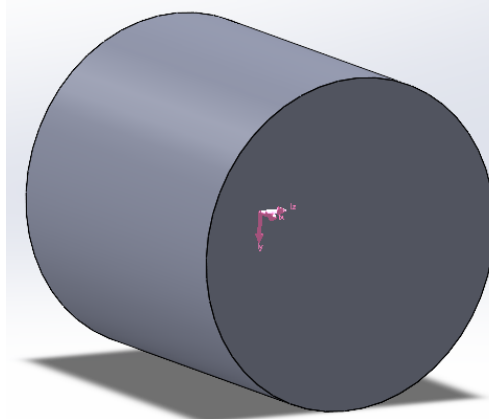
3D модель заготовки деталі «Втулка Рухомого Механізму»
